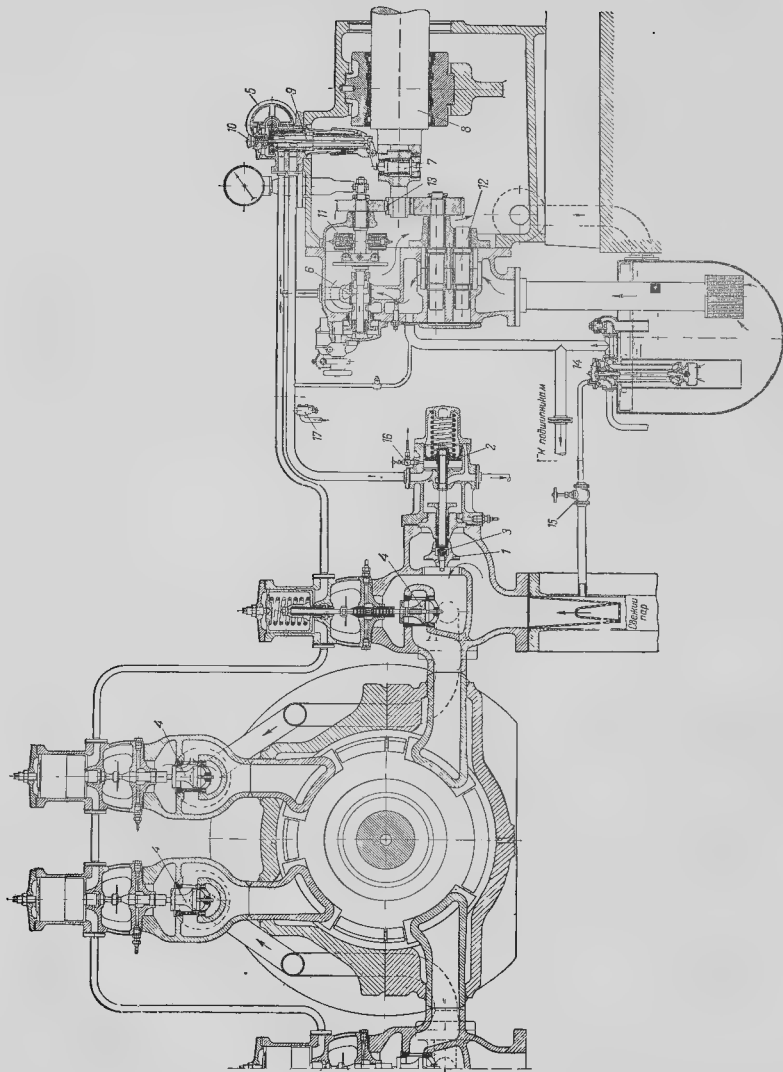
Схема регулирующего устройства турбины Броун-Бовера более новой конструкции.
